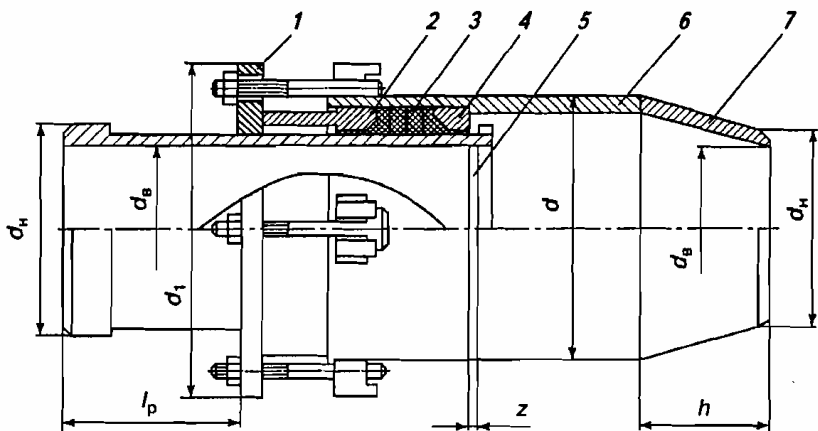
Односторонний сварной сальниковый компенсатор: 1 – нажимной фланец; 2 – грундбукса; 3 – сальниковая набивка; 4 – контрбукса; 5 – стакан; 6 – корпус; 7 – переход диаметров; Компенсирующая способность его составляет 250...400 мм
